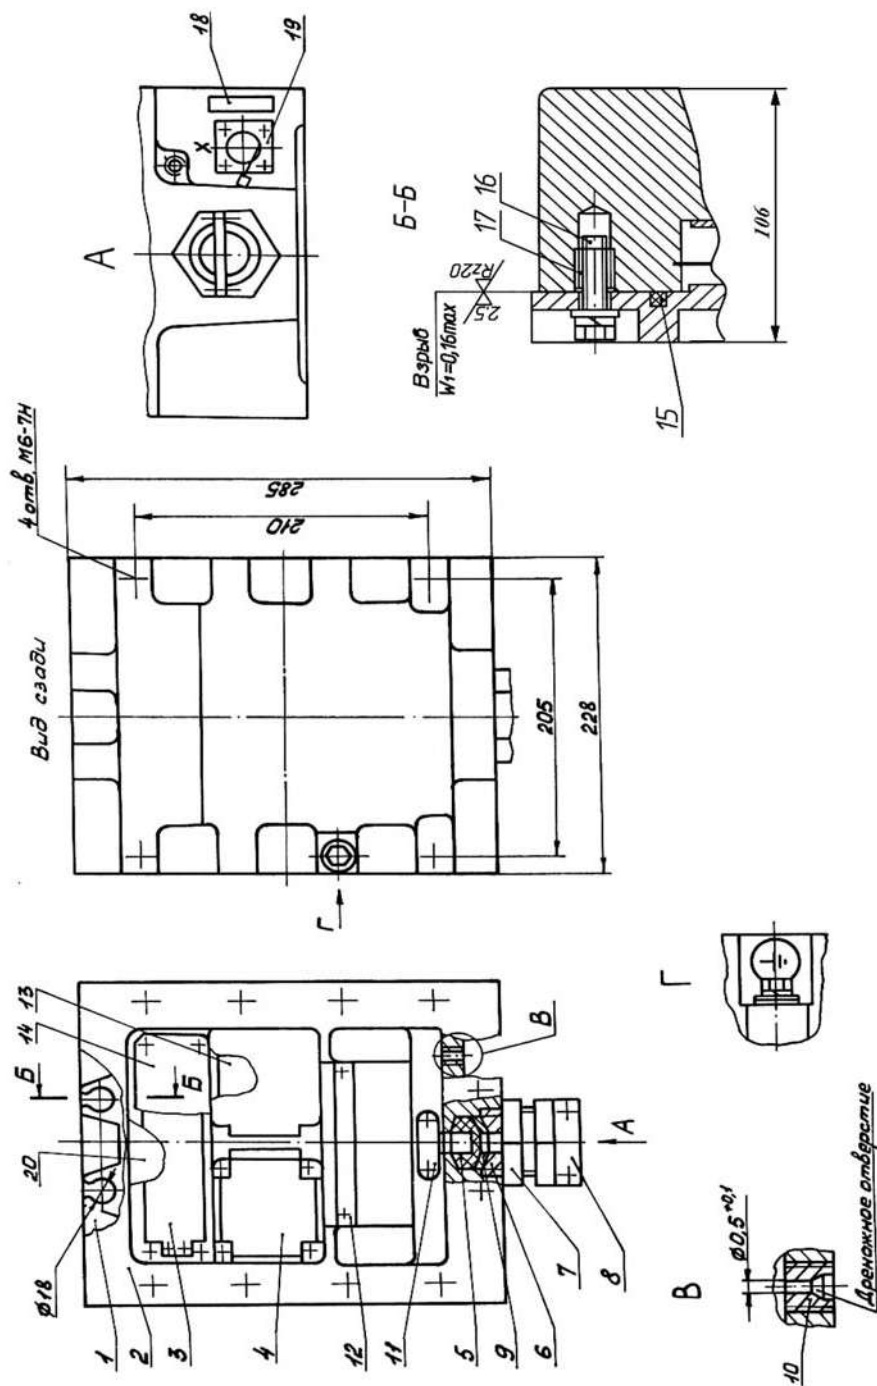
Преобразователь нормирующий. Внешний вид и габаритные размеры:
